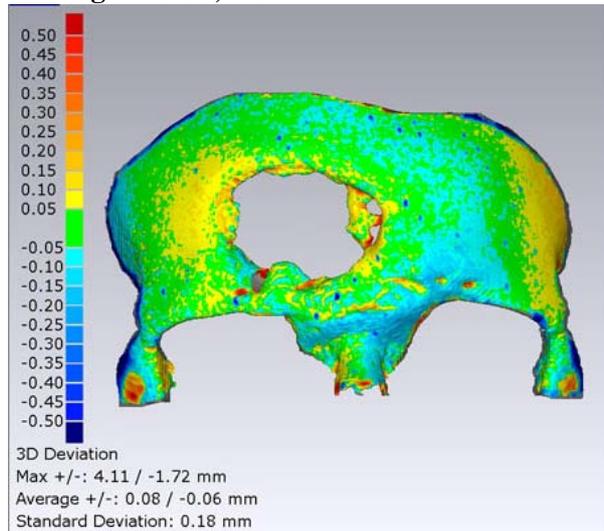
Precisão do protótipo fabricado por usinagem CNC de PU.
